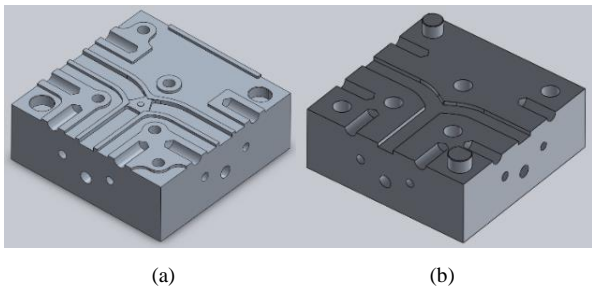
Modèles Solidworks des deux demi-coques : (a) Partie basse ; (b) Partie haute.
